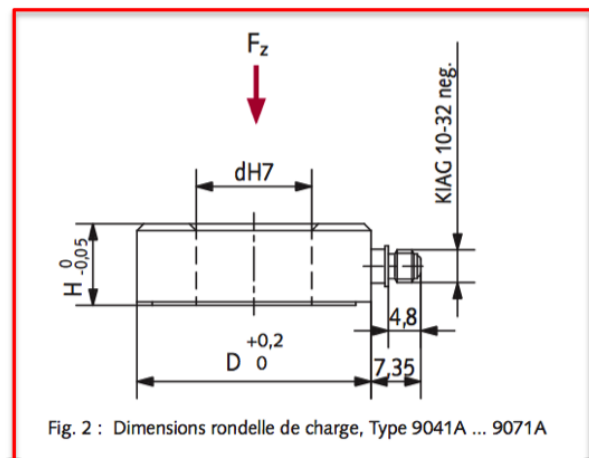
Dimensions rondelle de charge, Type 9041A ... 9071A
